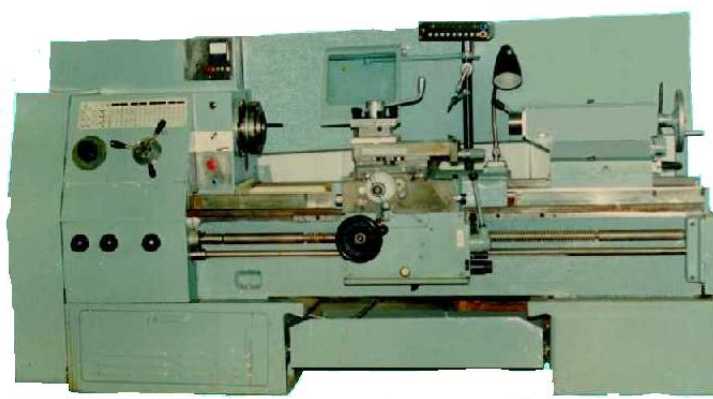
Станок токарно-винторезный ФТ-11
